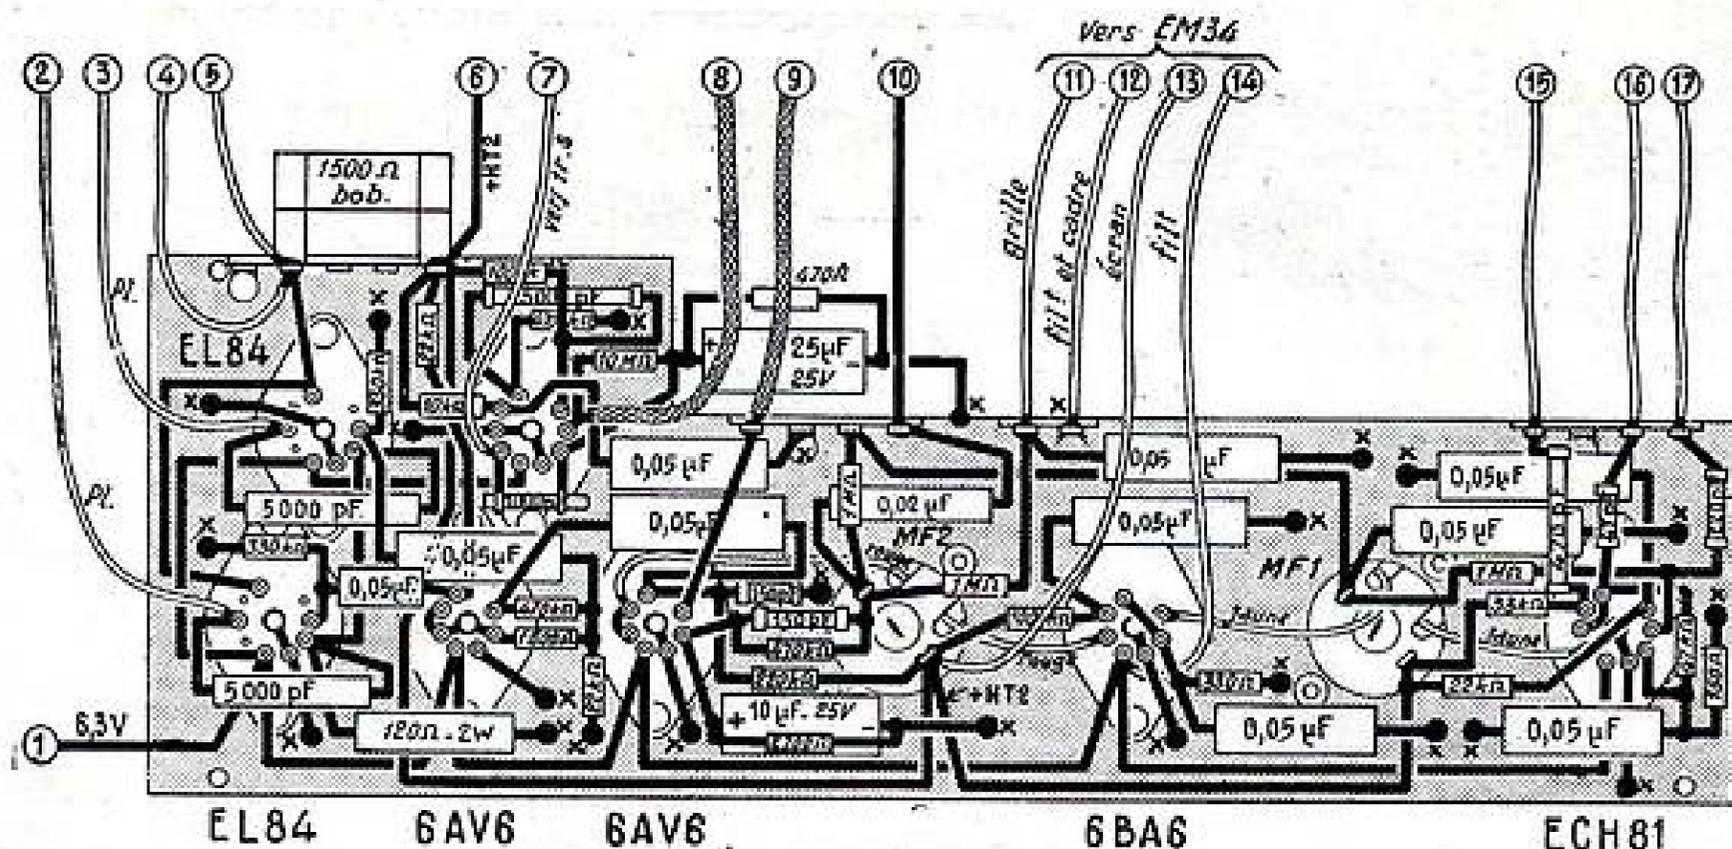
Plan de câblage de la platine pouvant être précablée.
